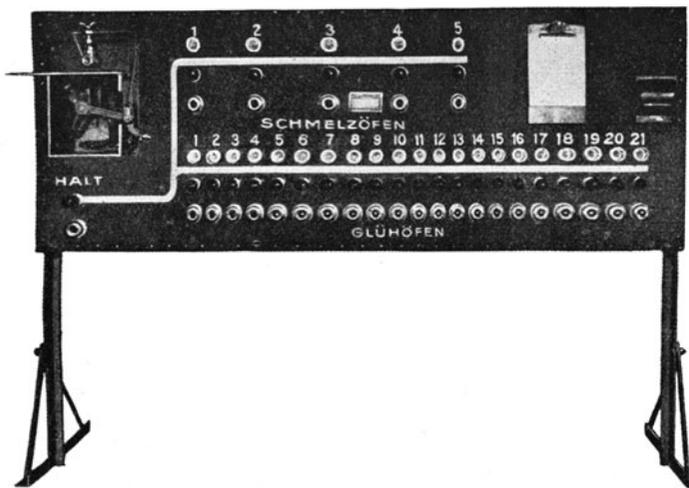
Schalttafel mit Druckknopfsteuerung der Grindle Fuel Equipment Co.
